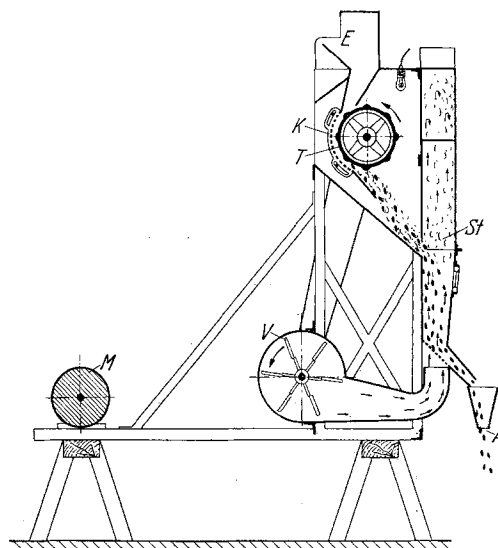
Längsschnitt durch die Dreschmaschine. E Einwurf, T Trommel, K Korb, St Steigsichter, A Auslauf für Körner, V Ventilator, M Motor.
